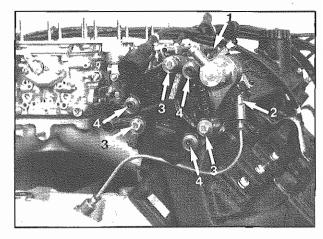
1 - Tubo depressione Vacuum pipe
